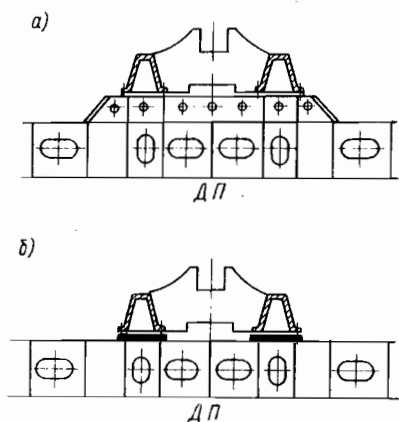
Типы фундаментов под главный двигатель: а — на настиле второго дна; б — встроенный в конструкцию двойного дна
